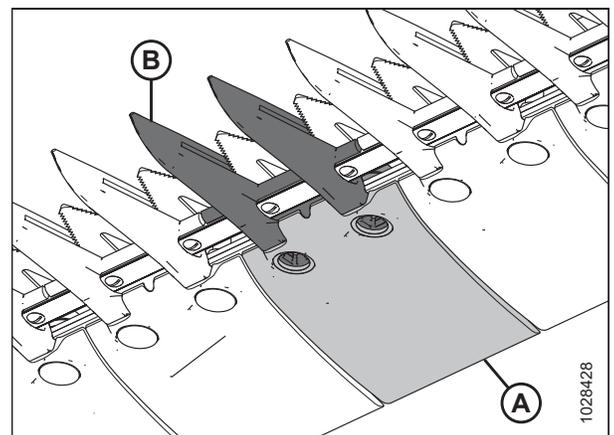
Doigts de couteau pointus et plaque d'usure
